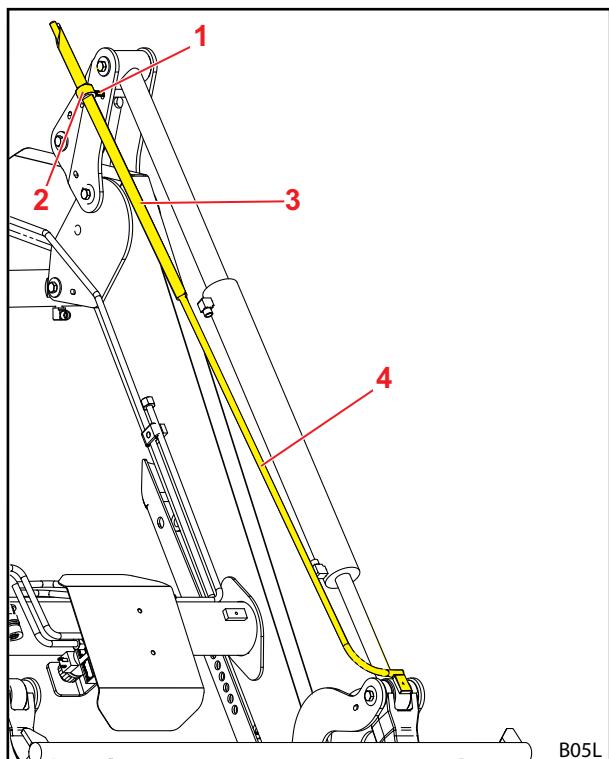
Sichtanzeige für Werkzeugeinstellung
